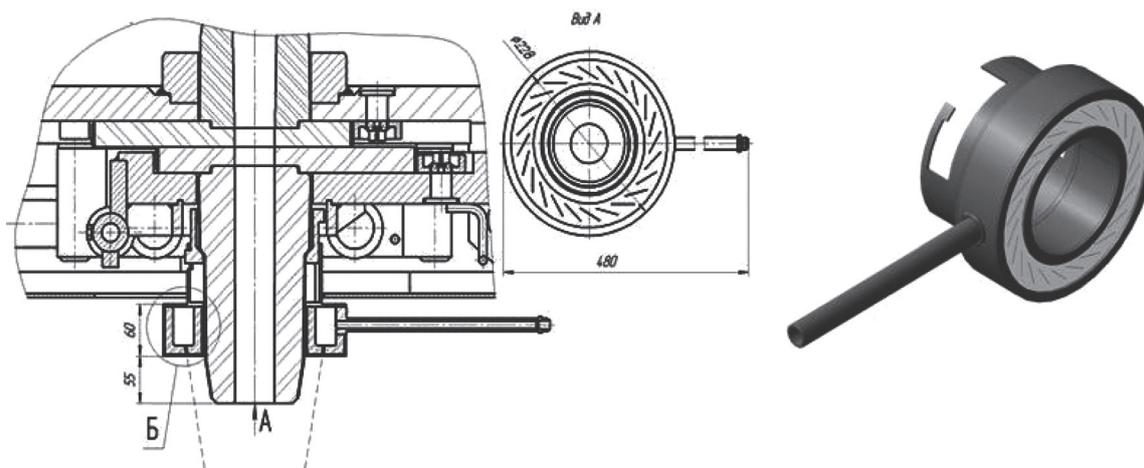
Устройство газодинамической защиты струи металла от вторичного окисления
